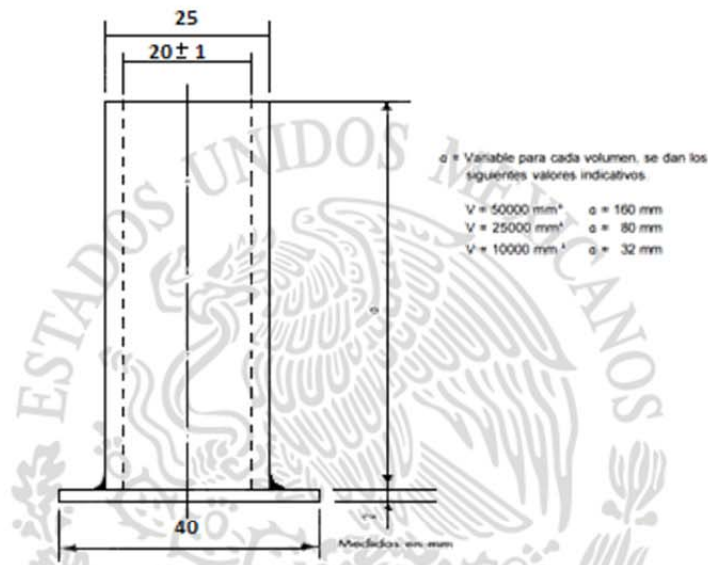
Dimensiones del recipiente para el ensayo (Norma NLT 335)
